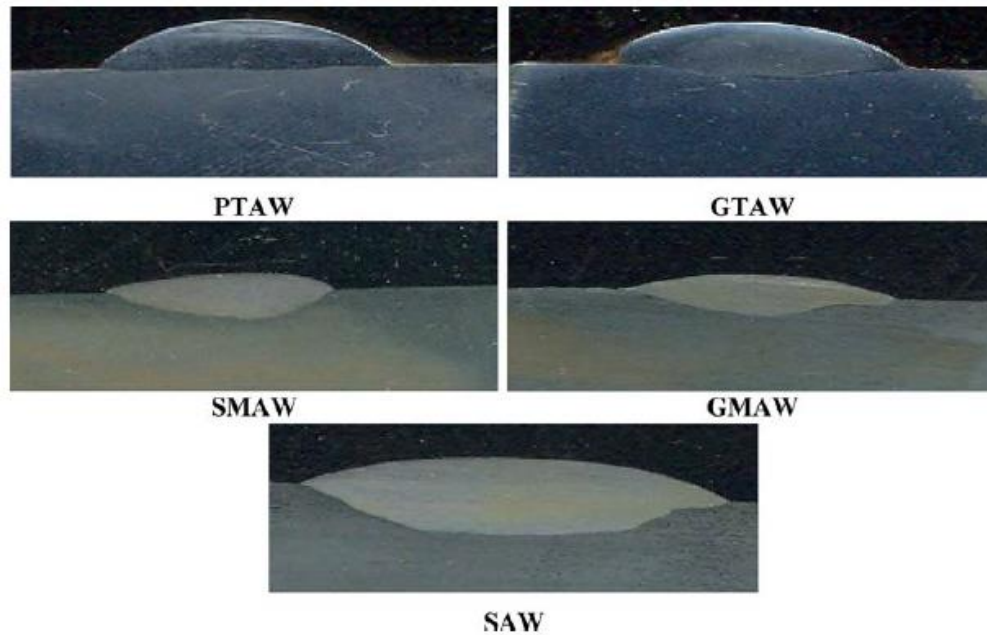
Geometrías de los cordones de soldadura para cada método
